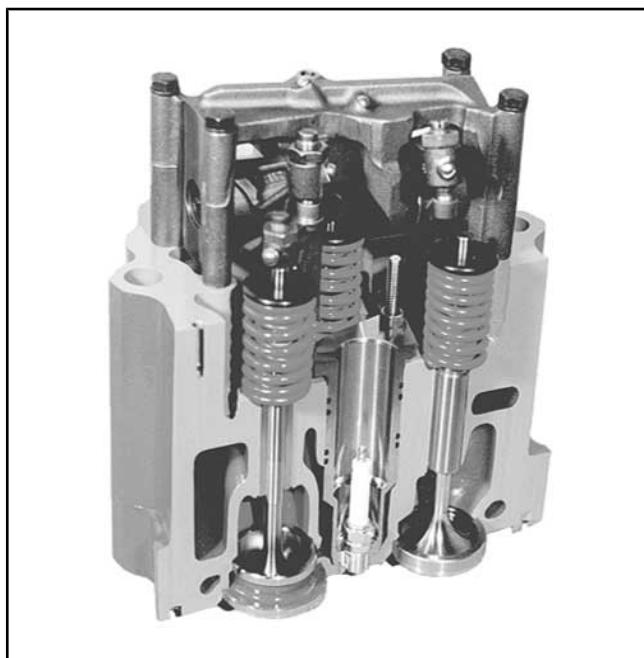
Головка цилиндра, вид в разрезе
